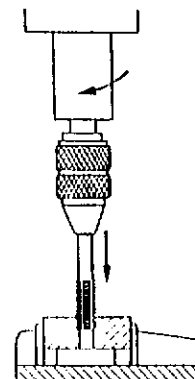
(izquierda). Roscado en la máquina de roscar.
